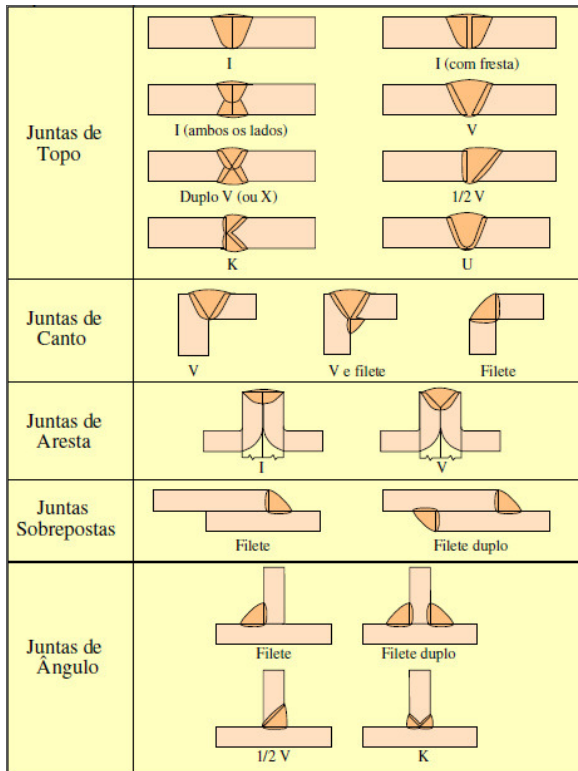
Combinação dos tipos de chanfros e juntas de soldagem
